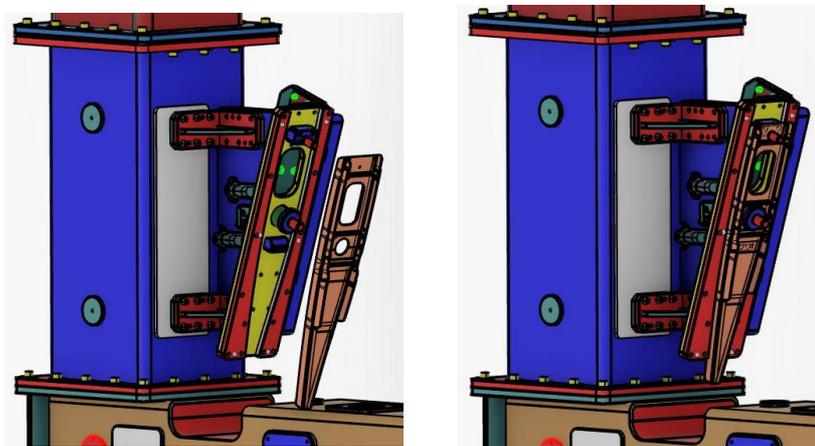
Wingtip explosionado y posicionado en la plantilla-útil del marco central
